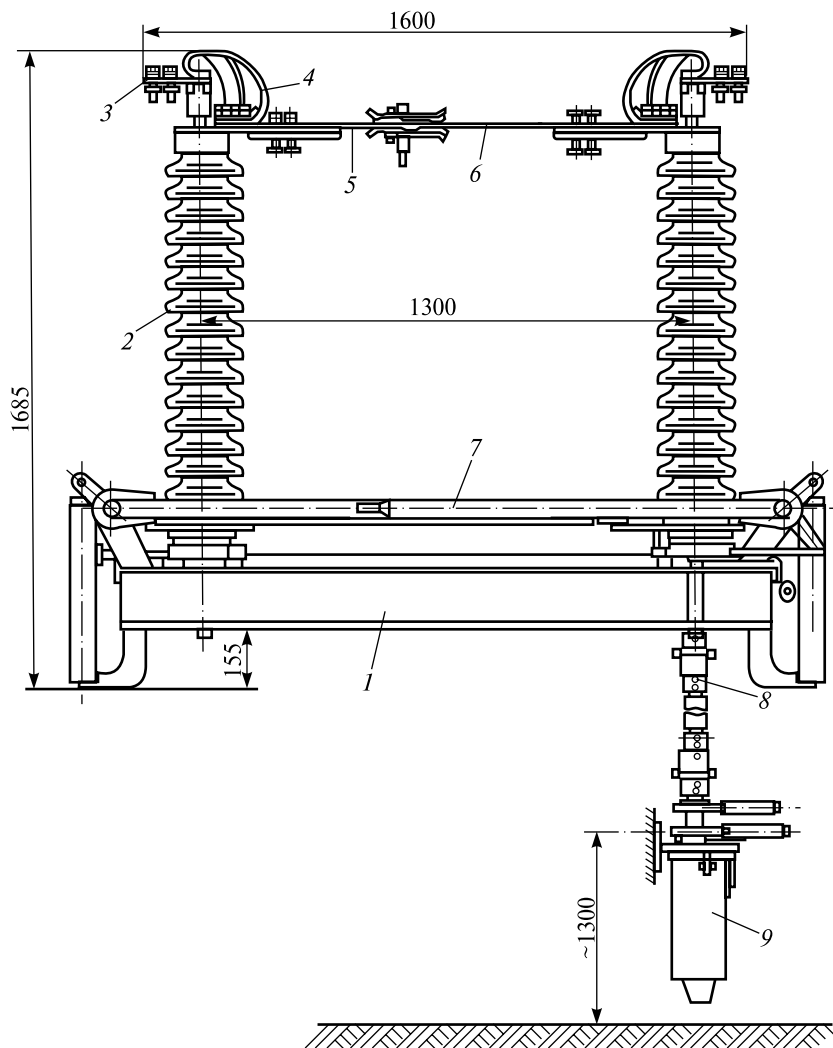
Разъединитель горизонтально-поворотного типа РНДЗ-2-110:
